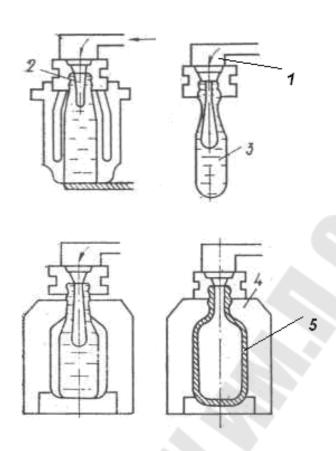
Схема выдувания стеклянной тары в форме: I — дутьевая головка; 2 — керн; 3 — набор стекла; 4 — форма; 5 — готовое изделие
